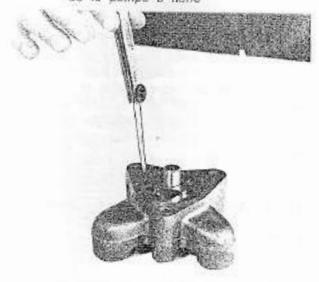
Contrôle du jeu entre rotor extérieur et son siège
